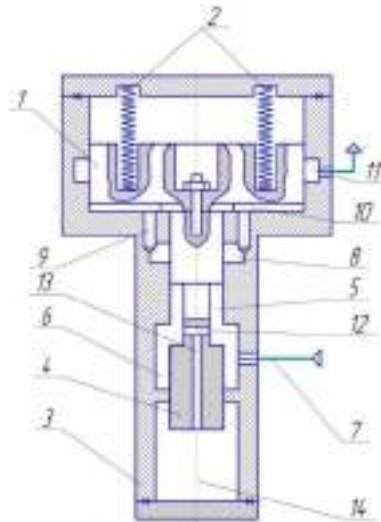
Пневмоімпульсний привод [16]: 1 – інерційна маса; 2 – силові пружини; 3 – корпус; 4 – двокромковий золотник; 5 – кільцева проточка; 6, 8, 11 – кільцева розточка; 7 – магістраль високого тиску; 9, 12, 13 – пневматичні канали; 10 – поршнева порожнина; 14 – акумулююча камера.
